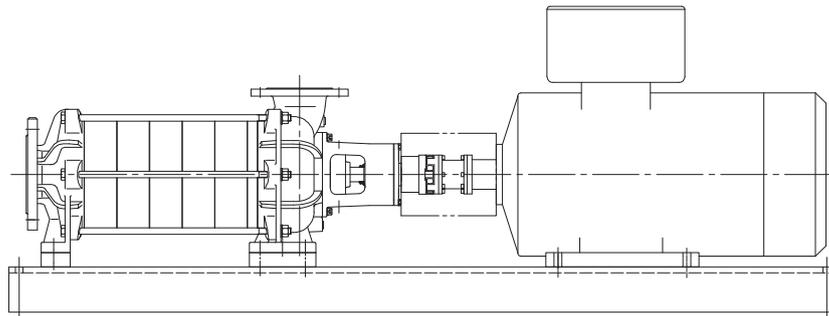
Ausbaustufe A, Pumpe mit Motor gekuppelt, auf Grundplatte montiert, mit Kupplungsschutz
